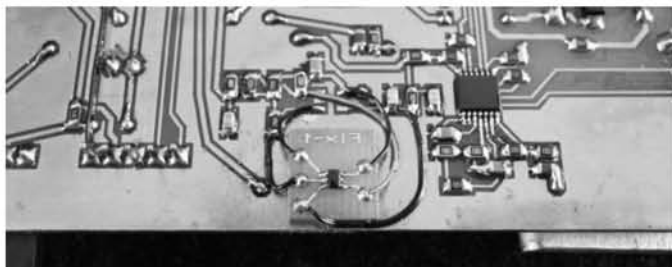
Tarjeta adaptadora SMD y cables wire-wrap.
